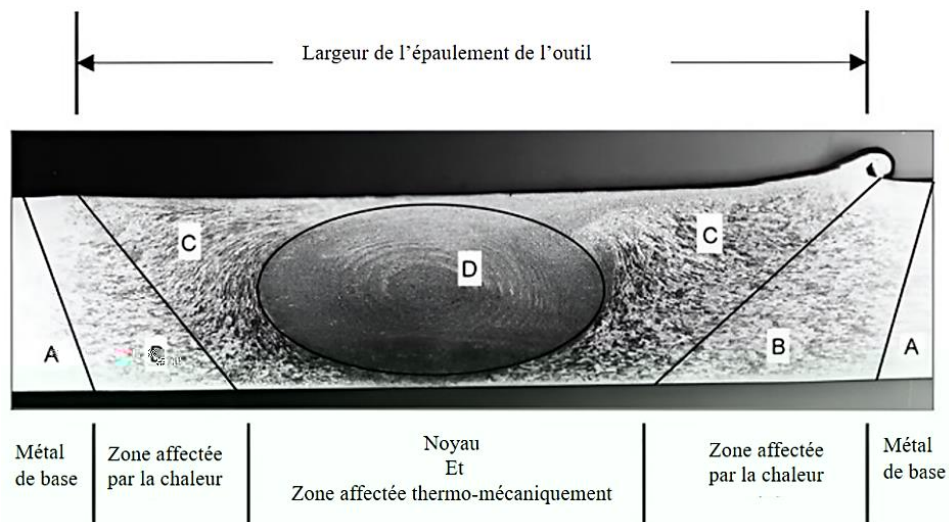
Vue microscopique du joint de soudure par friction [3].
